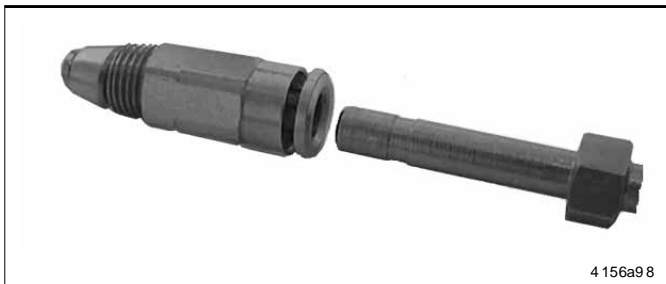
Rückschlagventil mit verstärkter Zange und Hochdruckschlauch
